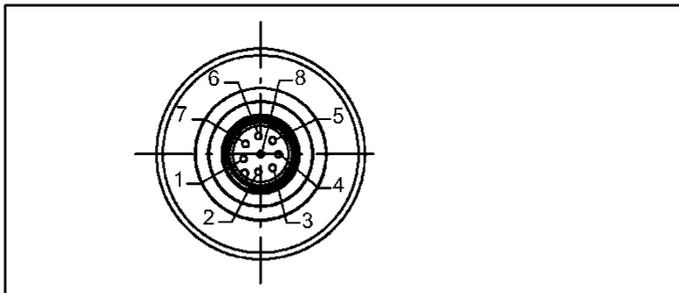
Соединительный разъем M12, 8-контактный штекер для преобразователей
